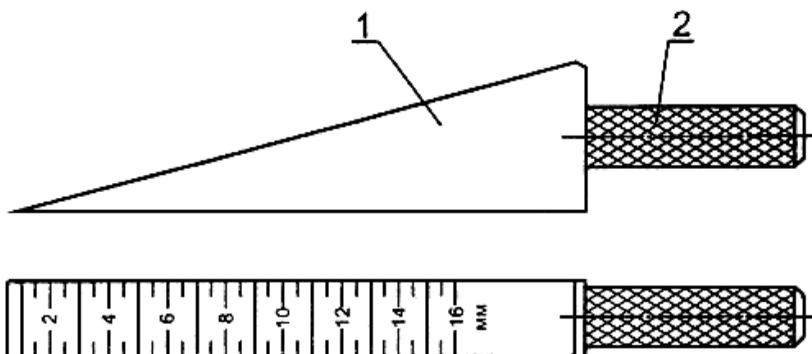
Общий вид клина для контроля зазоров (1 - клин; 2 - ручка)
